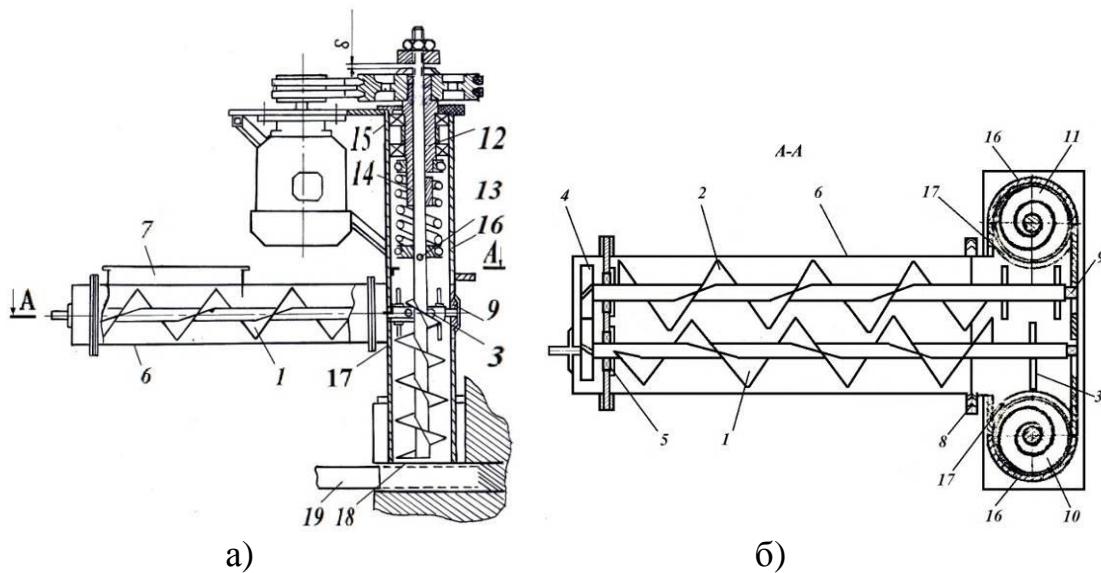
Конструкторська схема шнекового живильного пристрою:
